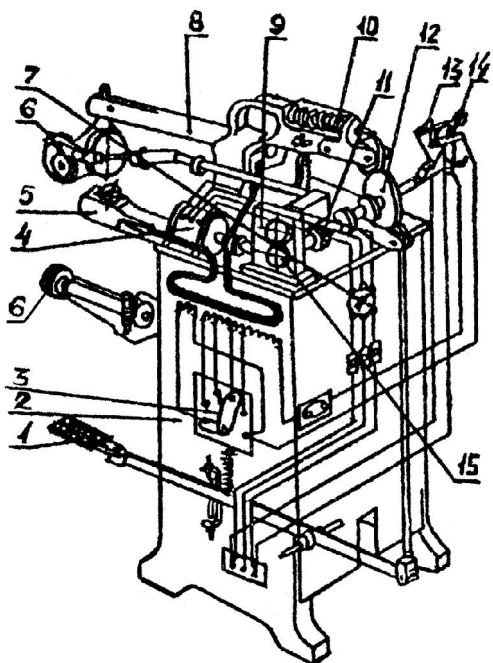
Схема машины для контактной точечной сварки МТ – 601.
